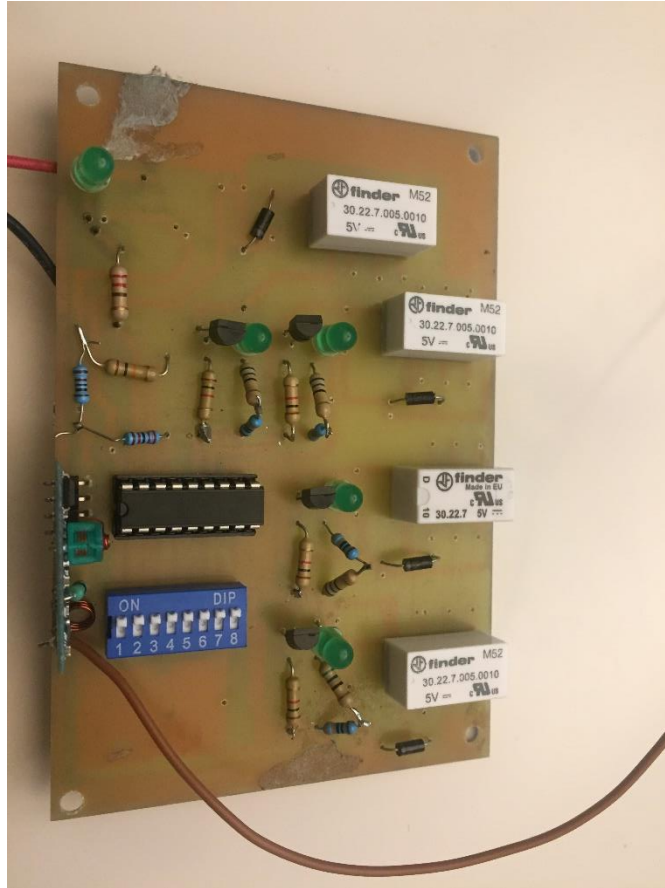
Placa receptora con los componentes soldados.
